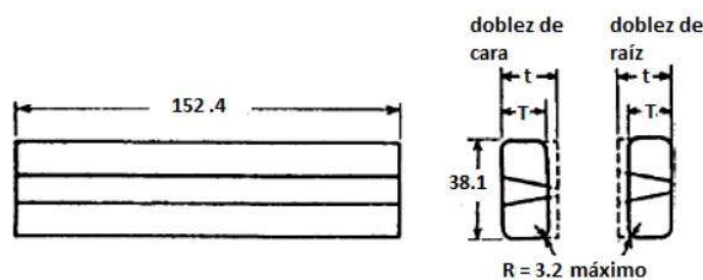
Dimensiones de probetas para doblado de cara
